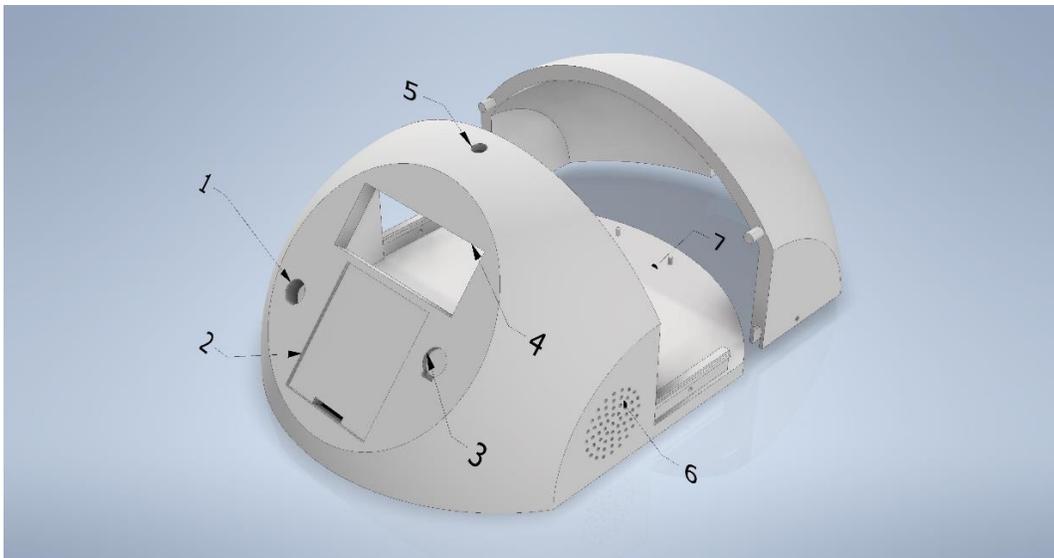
Diseño de Carcasa para montaje de Prototipo
